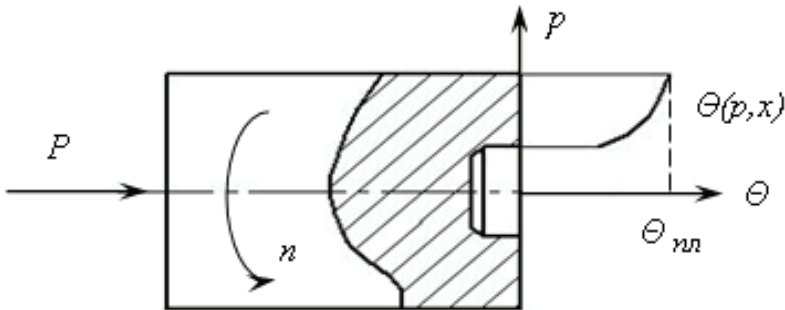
Схема распределения температуры по торцу заготовки при сварке трением
